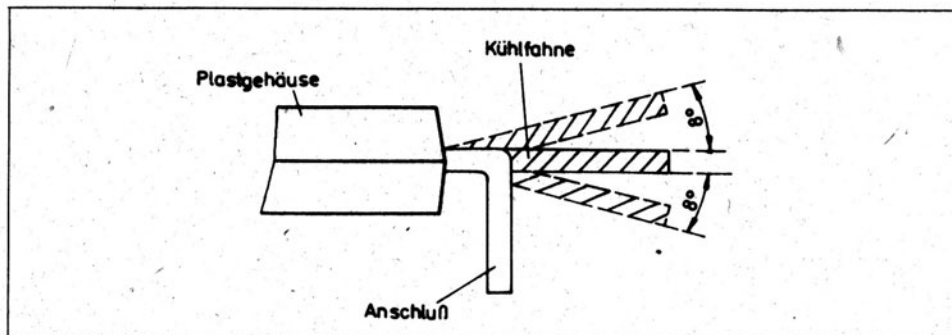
Zulässiger Biegewinkel der Kühlfahnen
